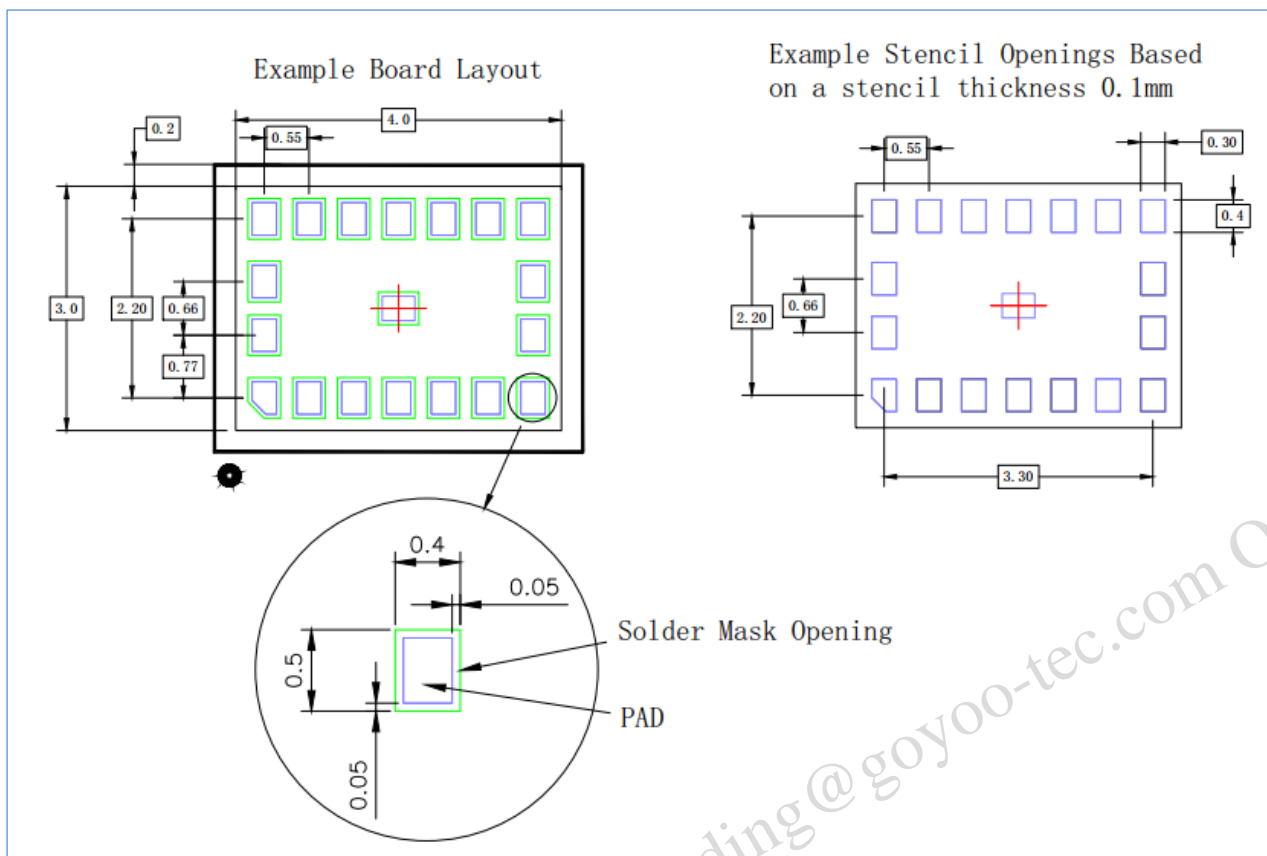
GH3018 PCB 封装设计示意图（底部视图）
